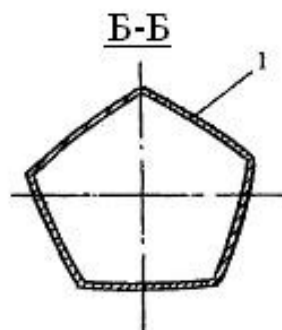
Сечение Б-Б корпуса 1 на рисунке 5 с центрами кривизны расположенными внутри корпуса
